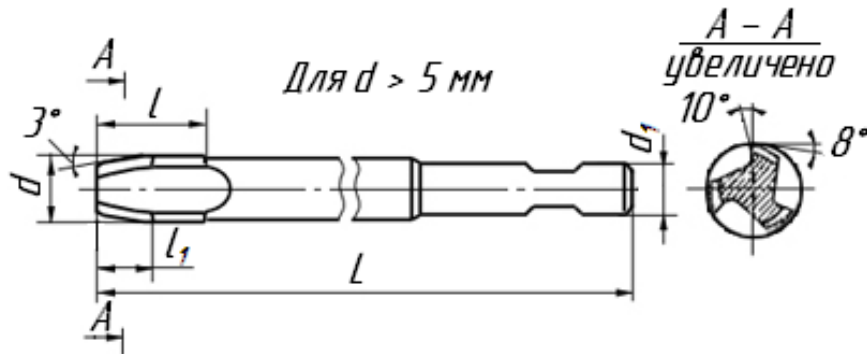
Метчик гаечный из быстрорежущей стали (ГОСТ 1604-71)
